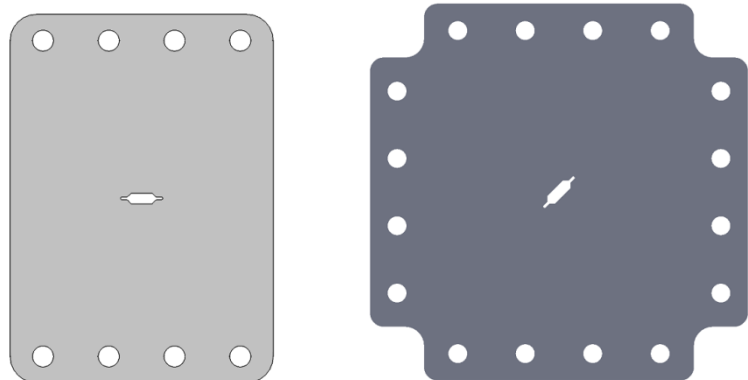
Vistas de Alzado de las Piezas con Entalla Horizontal y Entalla Girada
